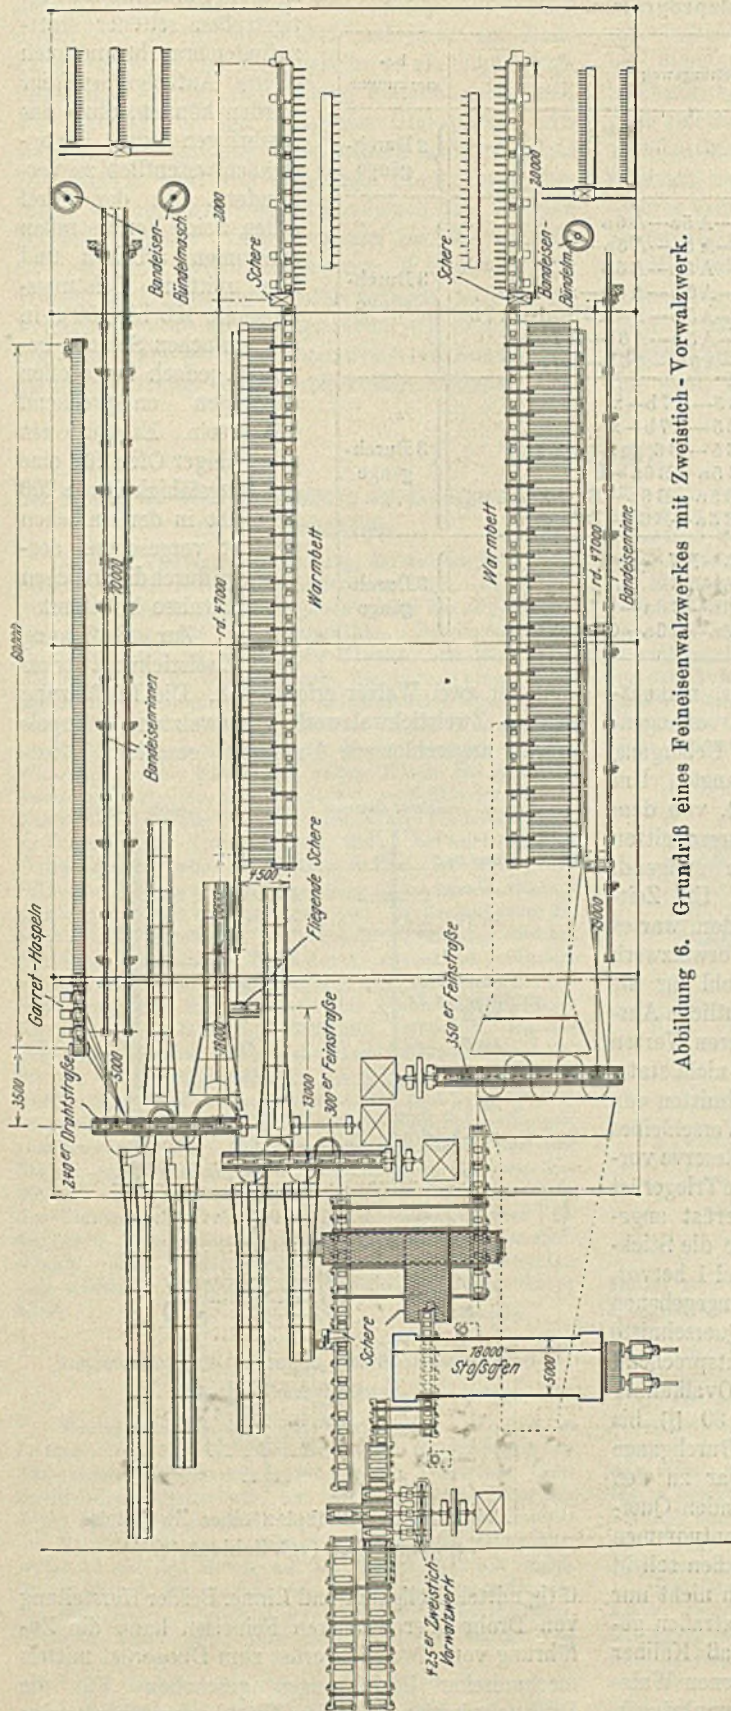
Grundriß eines Feineisenwalzwerkes mit Zweistich-Vorwalzwerk.
